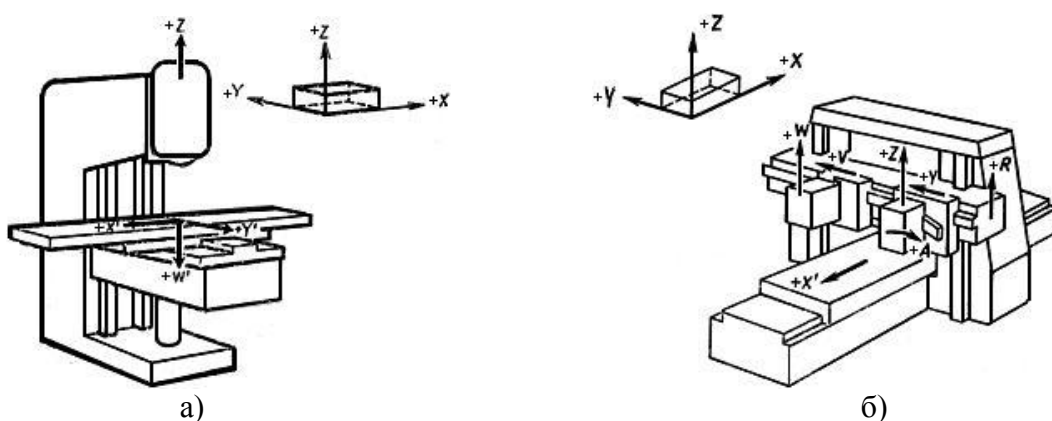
Оси координат во фрезерных станках с ЧПУ
